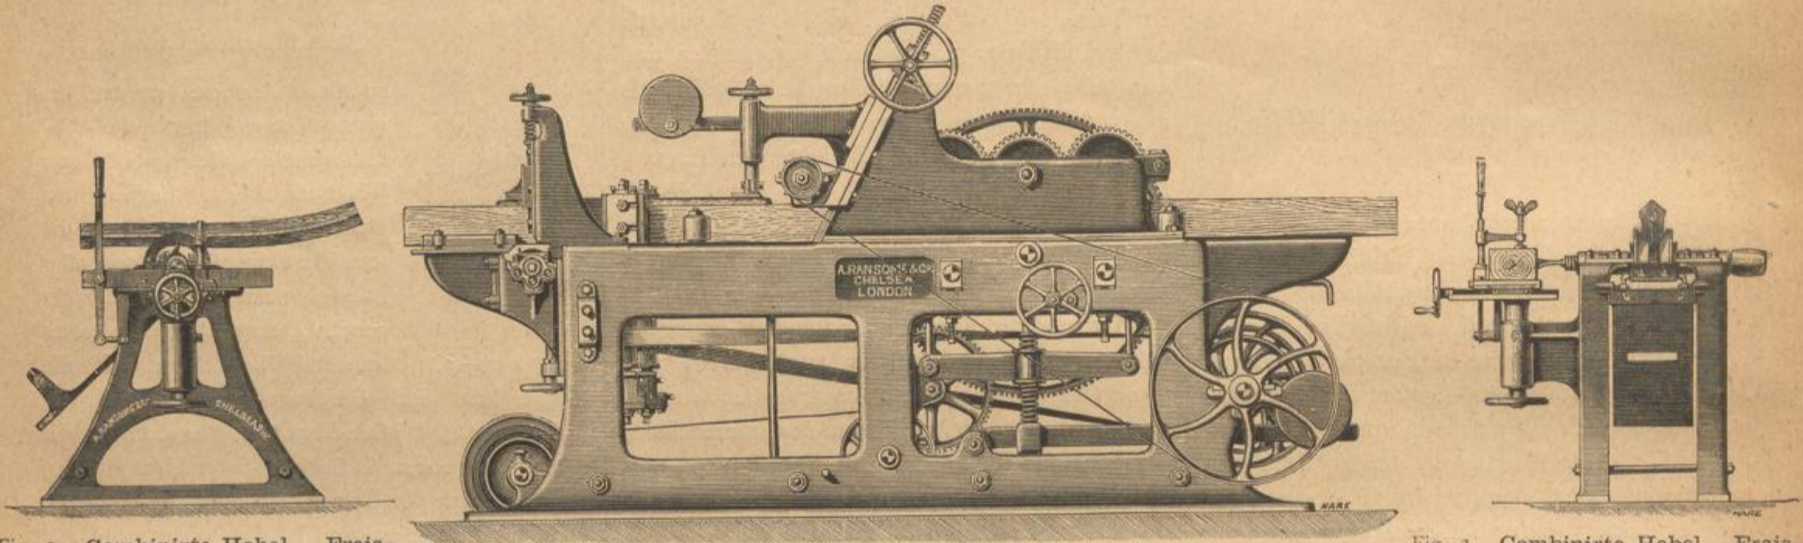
Combinirte Hobel-, Frais-, Kant-, Stemm- und Bohrmaschine.
